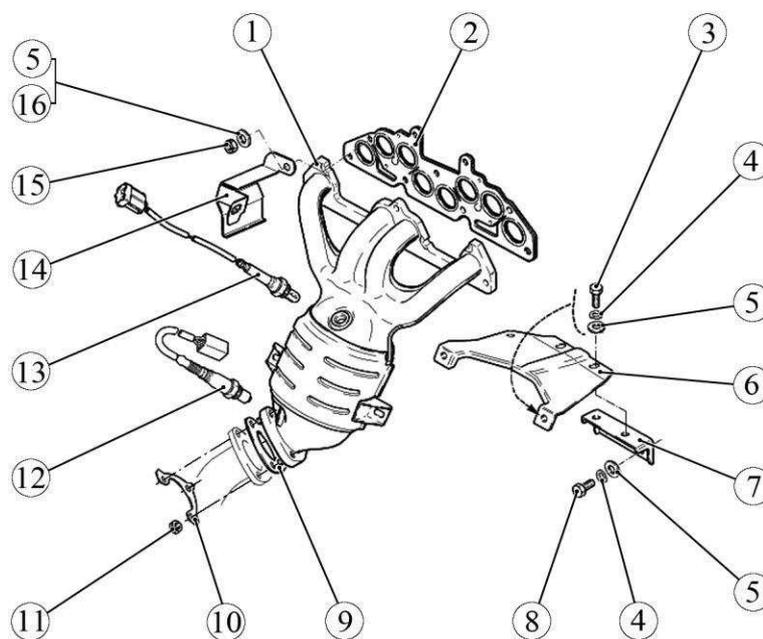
Установка приемной трубы глушителя с нейтрализатором в сборе:
